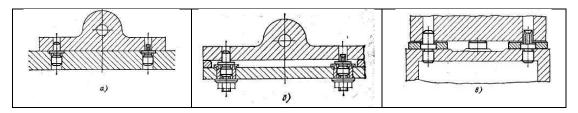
Примеры установки заготовки на два цилиндрических отверстия
